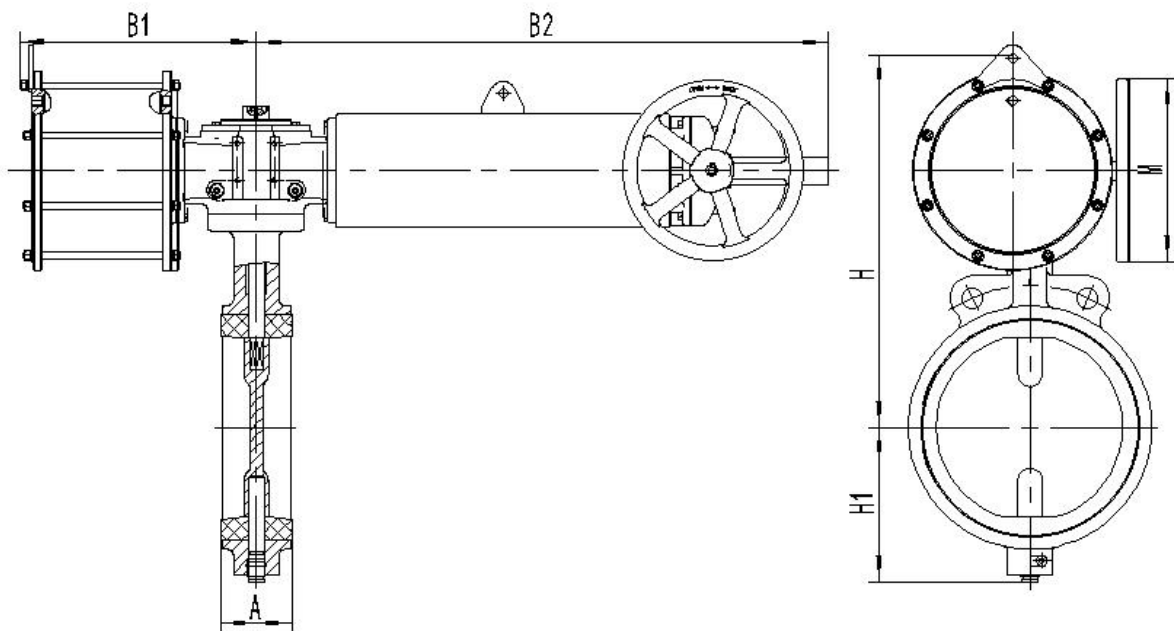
配 HCW27SR52~HCW40SR53 带伞齿手轮外形尺寸图 (FC)
